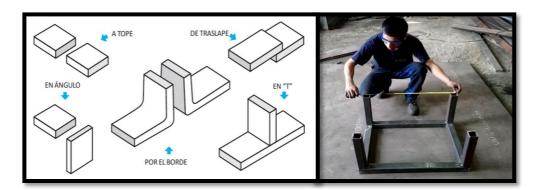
Preparación de Juntas para Soldadura (Soldexa, 2012, p. 53)
